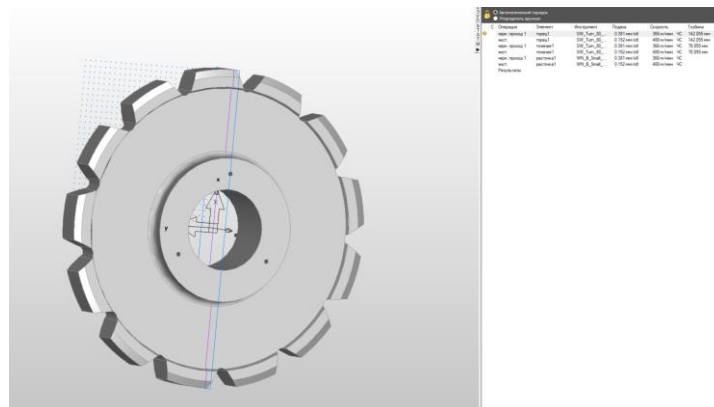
Список операцій обробки деталі «Зірочка»
